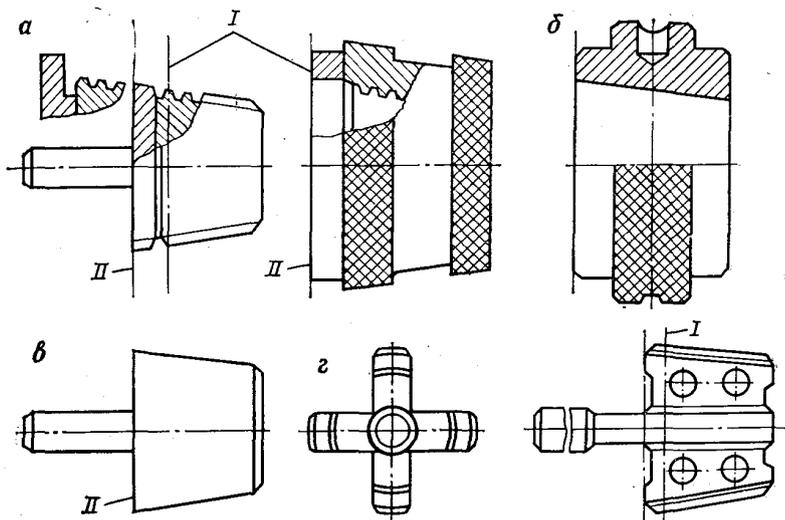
Калибры для проверки резьбы буровых труб и муфт к ним:
